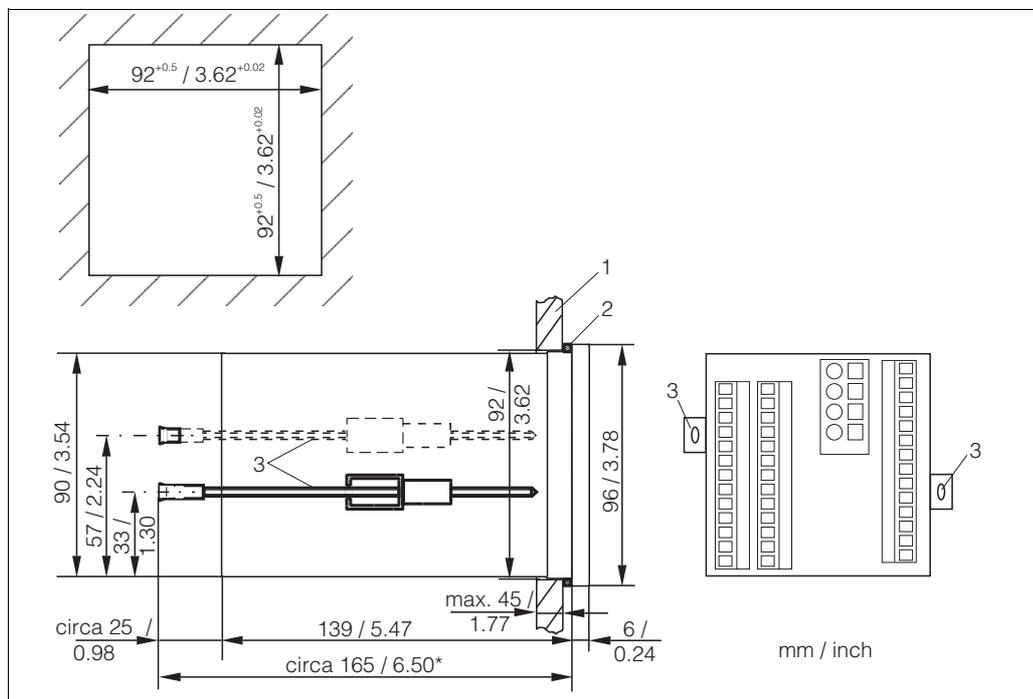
Fissaggio del trasmettitore per montaggio a fronte quadro
